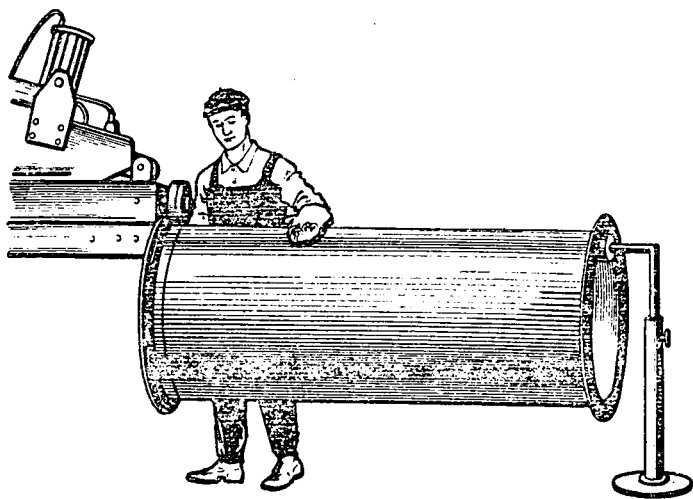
Рабочий момент офланцовки звена воздухопровода круглого сечения на зигмашине ЗМ-4
